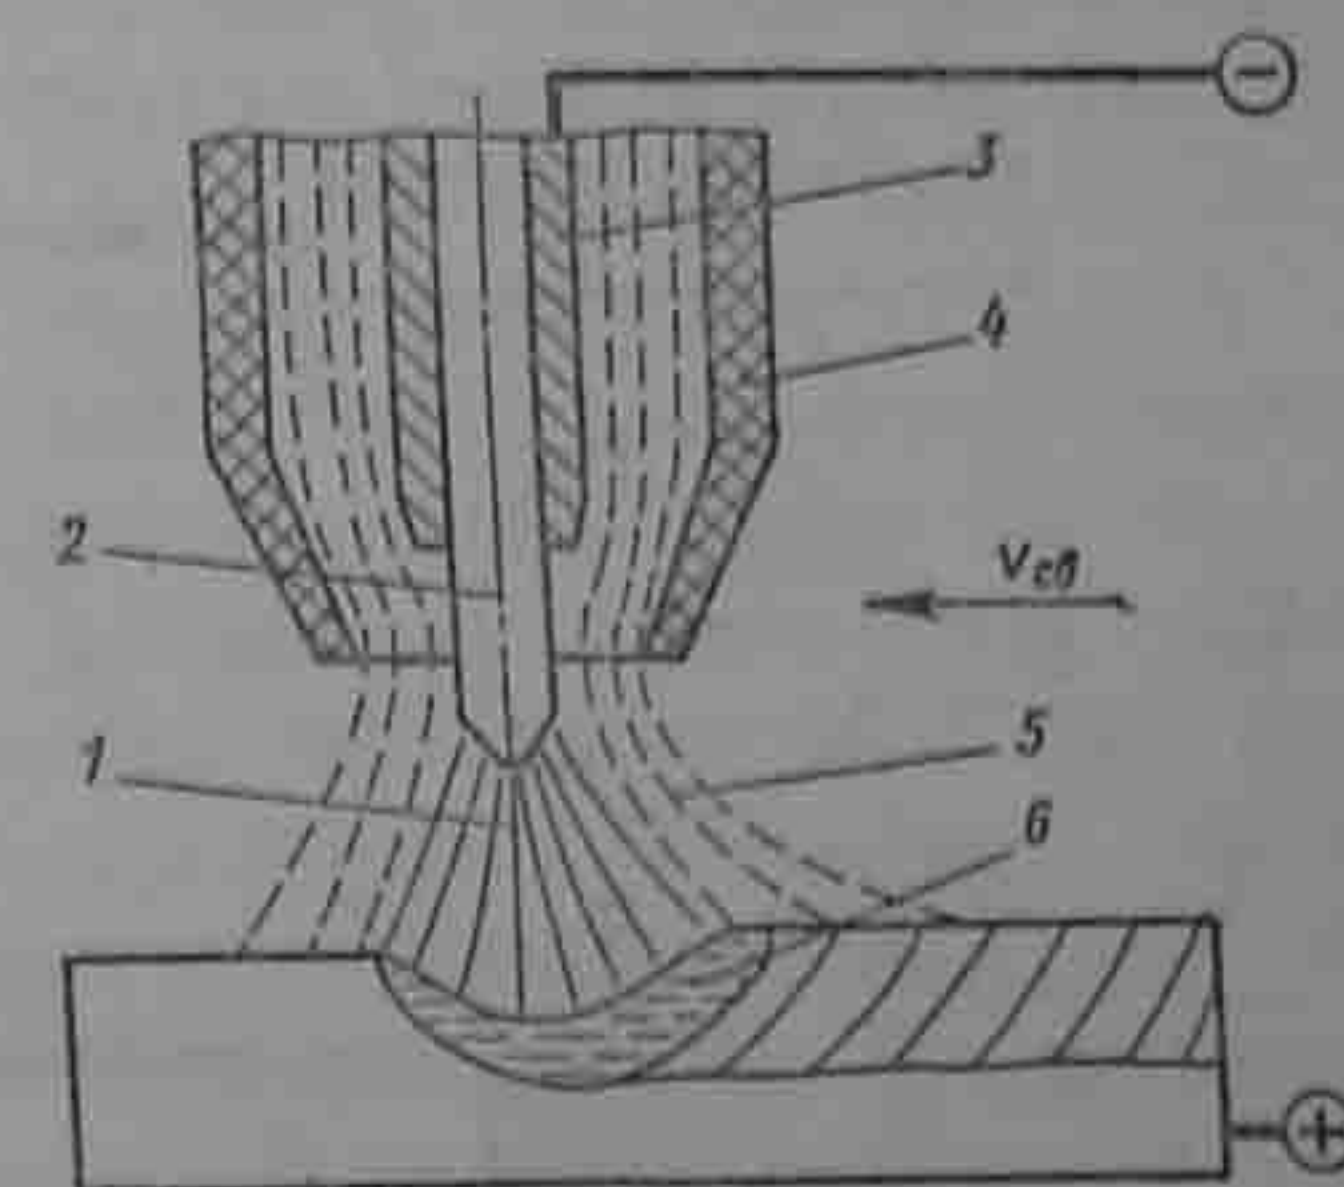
Схема сварки в атмосфере защитных газов
